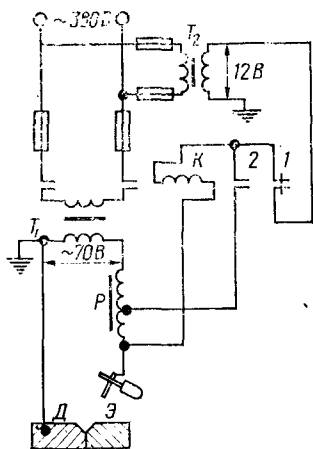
Схема автоматического отключения сварочного трансформатора при разрыве цепи:
